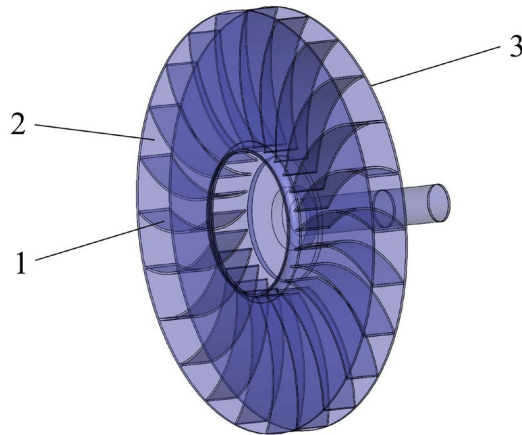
Рисунок робочого колеса вентилятора з його конструктивними елементами: 1 – лопатки; 2 – покривний диск; 3 – диск
